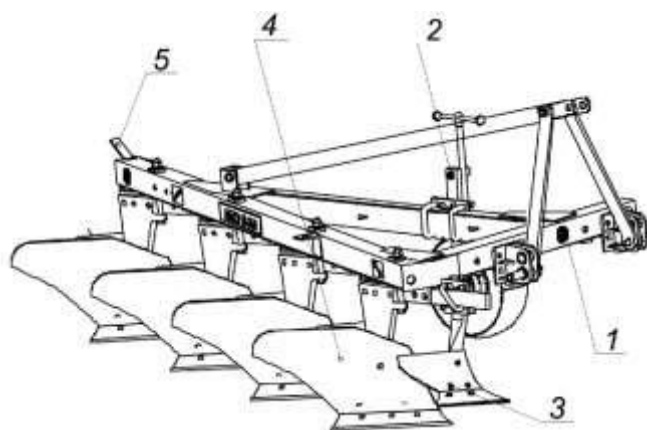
Плуг чотирьох корпусний навісний ПЛН-4-35: 1 – рама; 2 – механізм колеса; 3 – передплужник; 4 – корпус.
